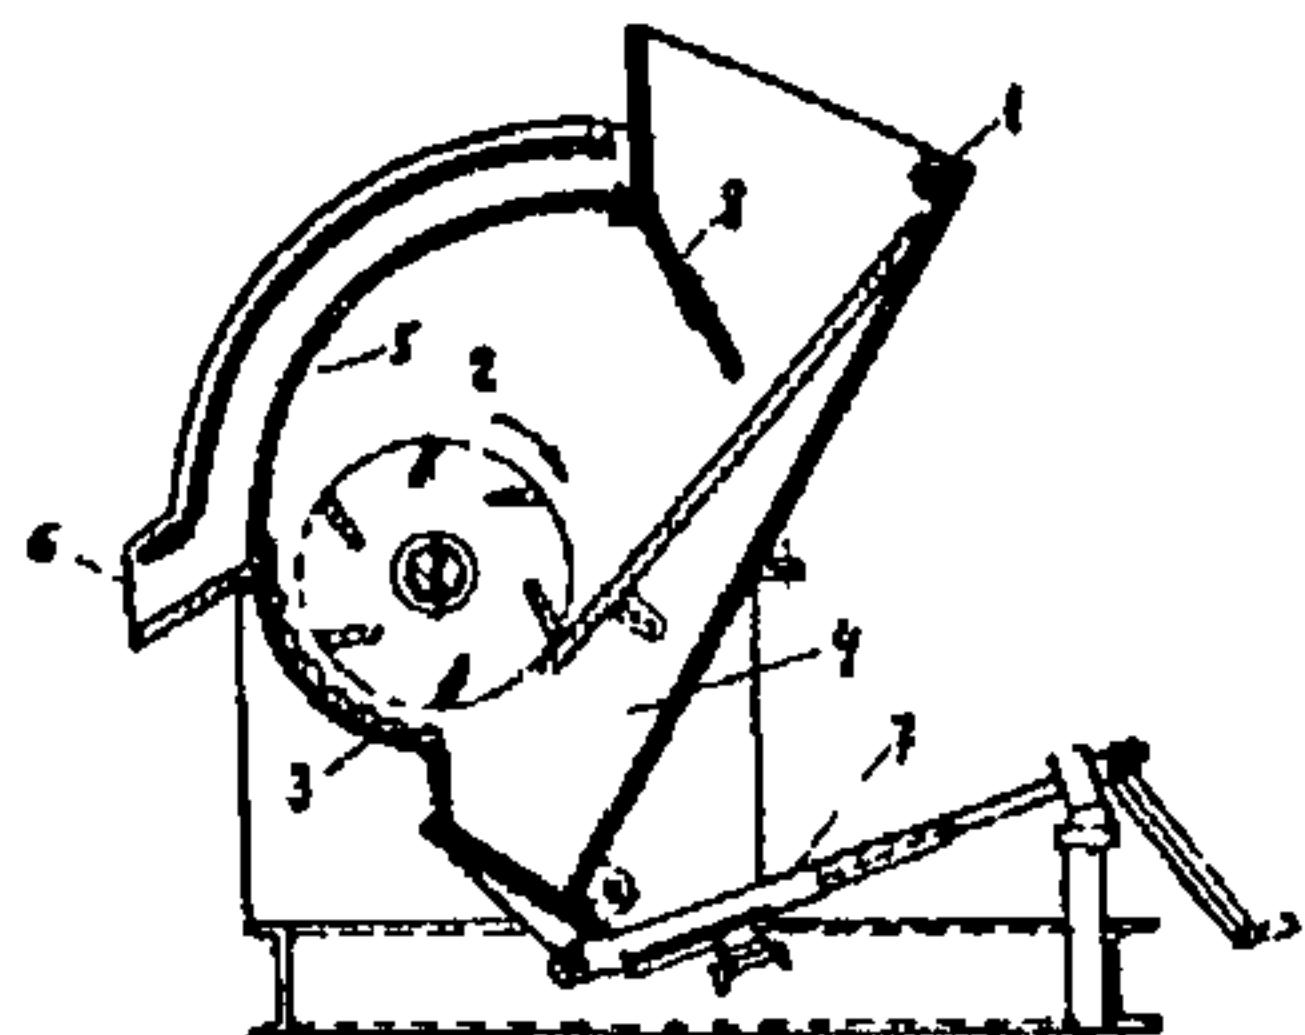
Фрезерно-струйная мельница ФСМ-3:
